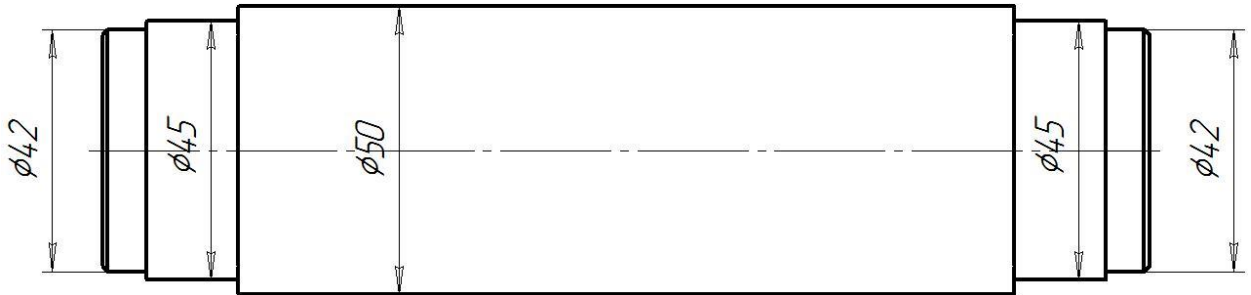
Конструкція четвертого вала коробки подач
